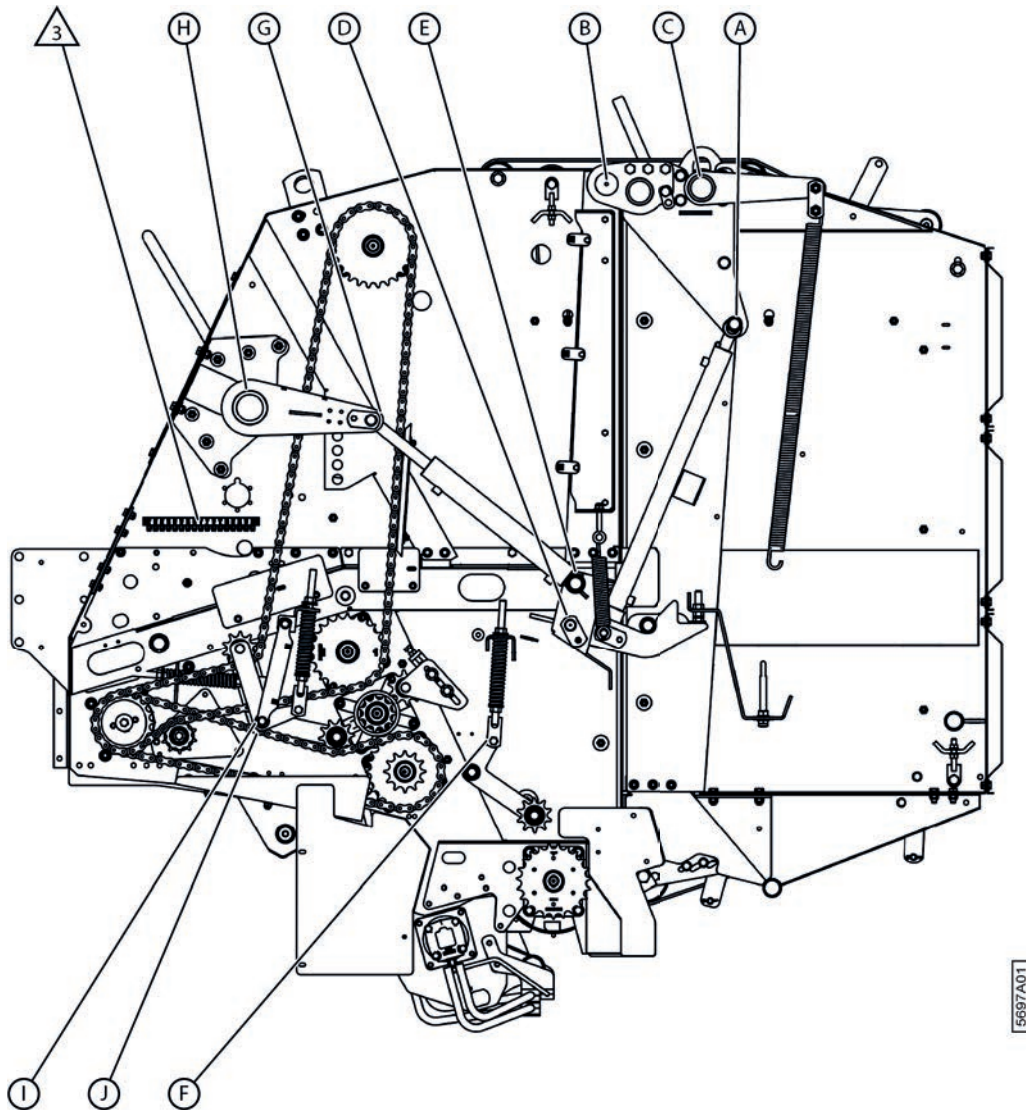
Aperçu des points de graissage du côté gauche de la cage
